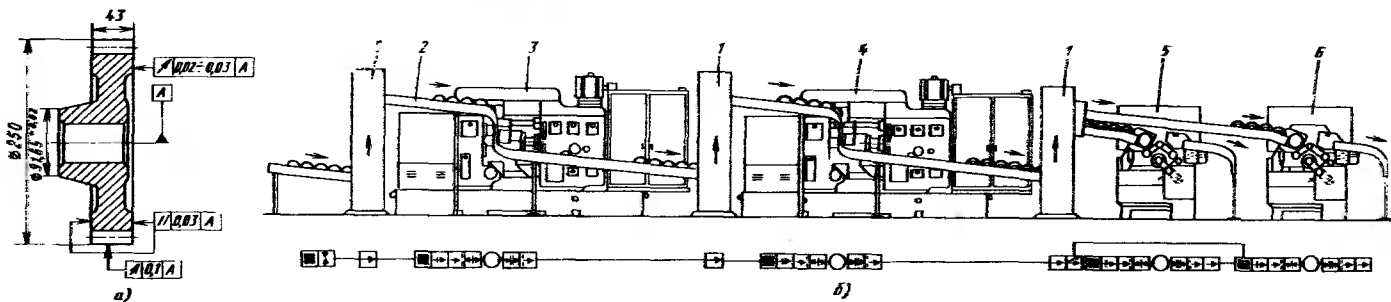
Схема автоматической линии для изготовления заготовок зубчатых колес типа диска
